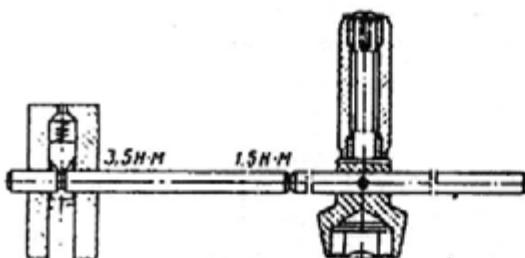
Контрольное приспособление проверки момента трения (сдвига) подшипников ведущей шестерни редуктора
